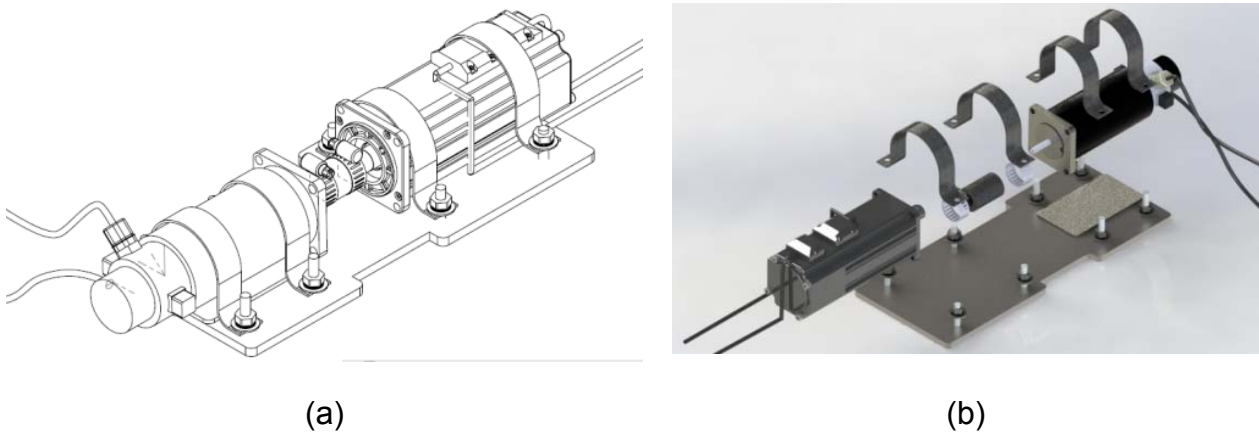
(a) Vista frontal de la plataforma experimental. (b) Explosivo con los componentes de la plataforma experimental.
